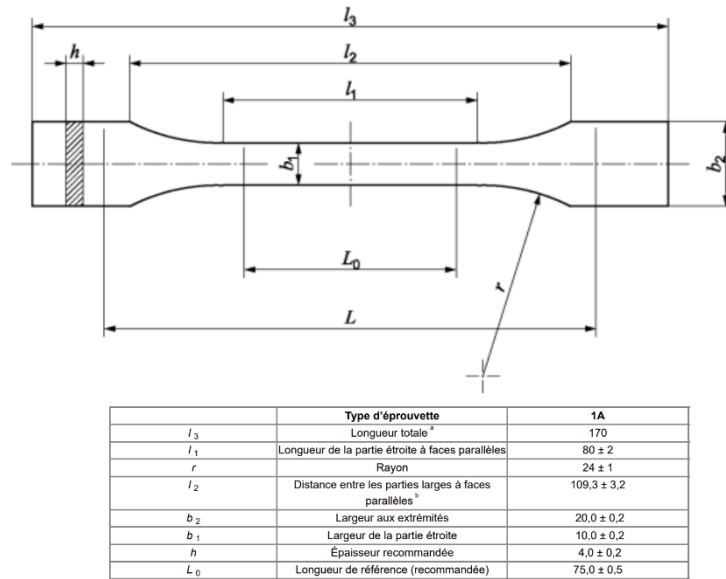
Dimensions des éprouvettes ISO 527-2/1A, en millimètres, d'après [3].
